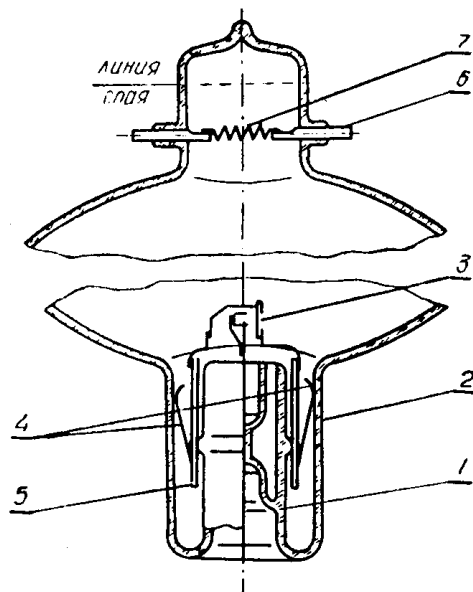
Конструкции инжекторного и геттерного узлов: 1 — ножка, 2 — патрубков камеры, 3 — инжектор, 4 — пружинящие контакты, 5 — анодные траверсы, 6 — геттерный вывод, 7 — титановая лента.
